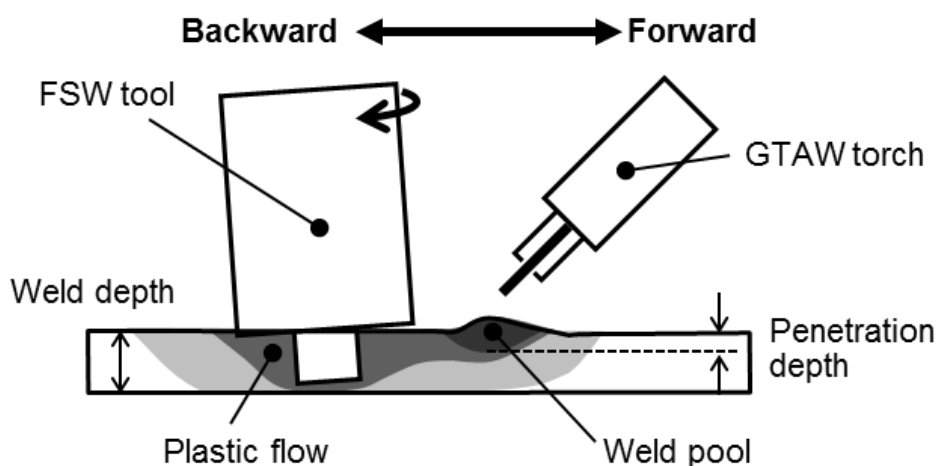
GTAW-FSW ハイブリッド溶接法の模式図
